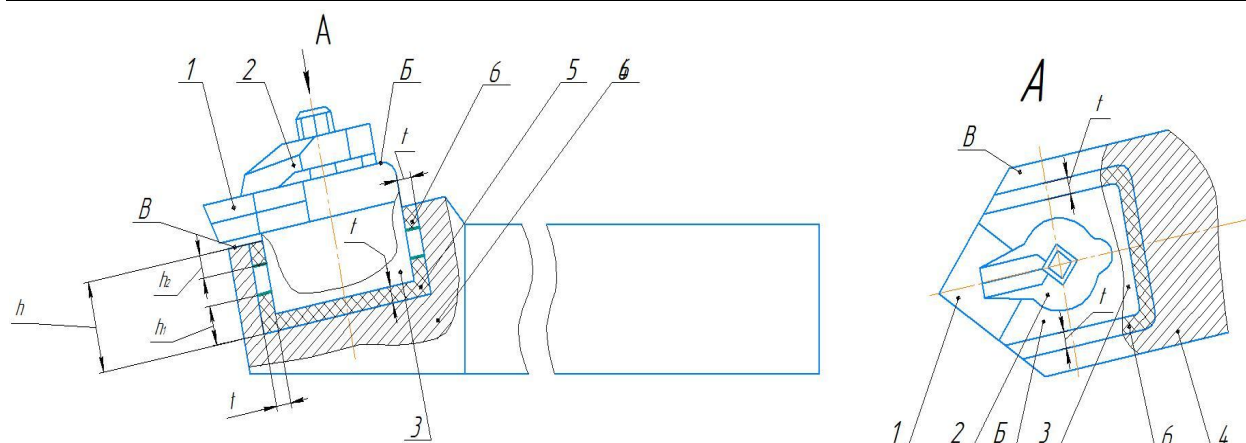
Универсальный демпфирующий резец: 1 – режущая пластина; 2 – узел крепления пластины; 3 – оправка; 4 – державка; 5 – полувставка-подпятник; 6 – полувставка, меньшей жесткости
